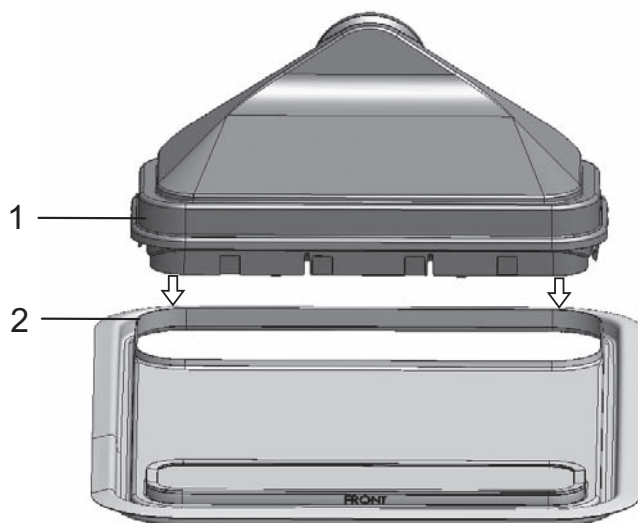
Установка воздушной коробки на крышку резервуара для воды
